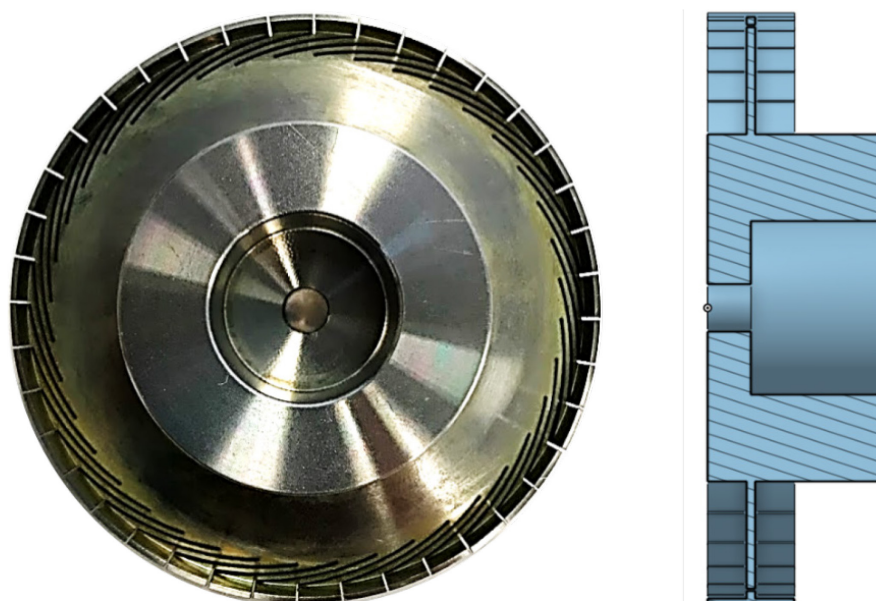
Vue de dessus du prototype fabriqué (gauche) et vue en coupe d'un dessin 3D (droite)
